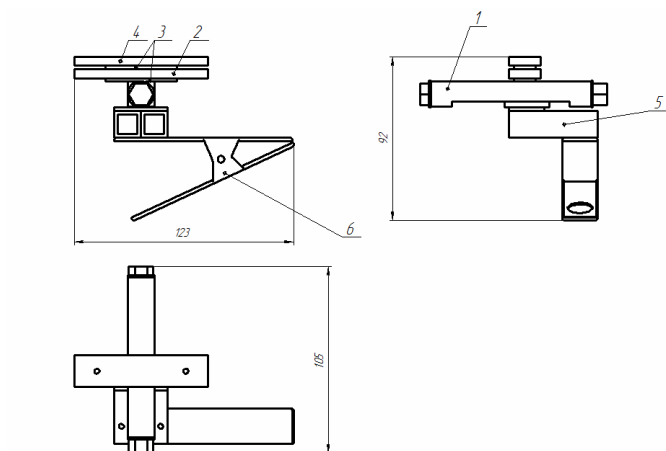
Конструкция и габаритные размеры одного плеча разделённого токоподвода
